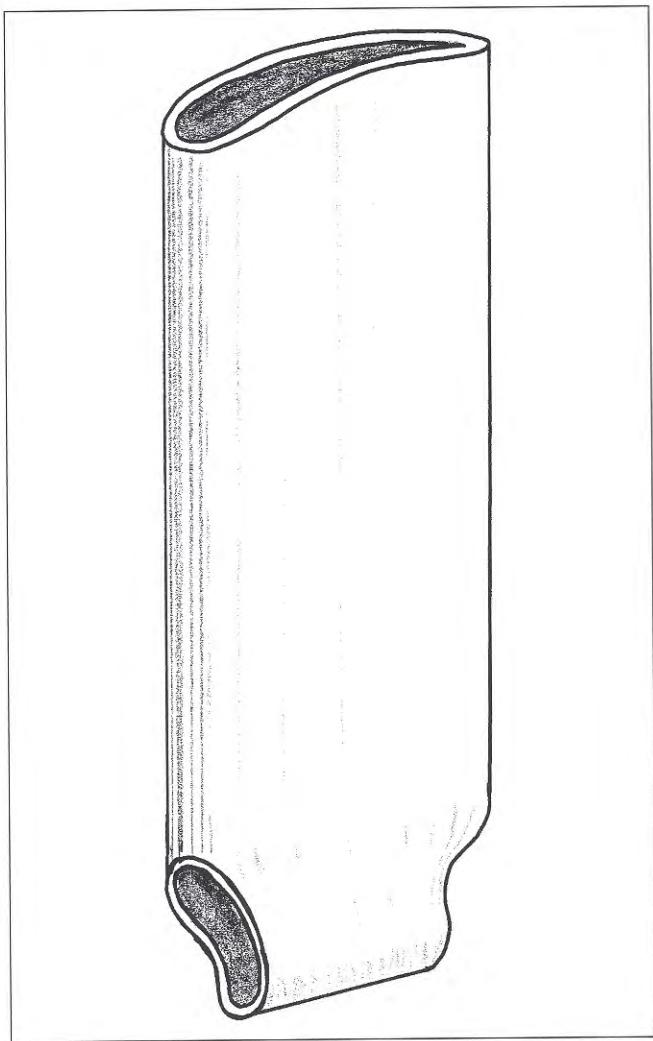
Полая лопатка турбины Topfschaufel для двигателя 109-011 А-0
